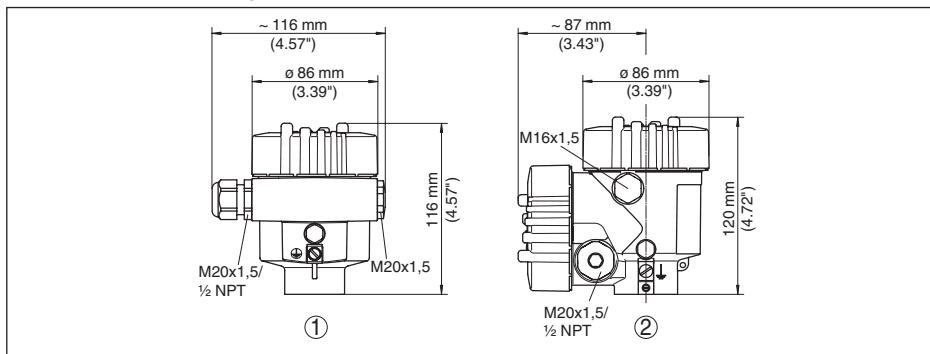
Корпуса в исполнении IP 66/IP 68 (0,2 bar) - с установленным модулем индикации и настройки корпус выше на 9 mm/0.35 in
